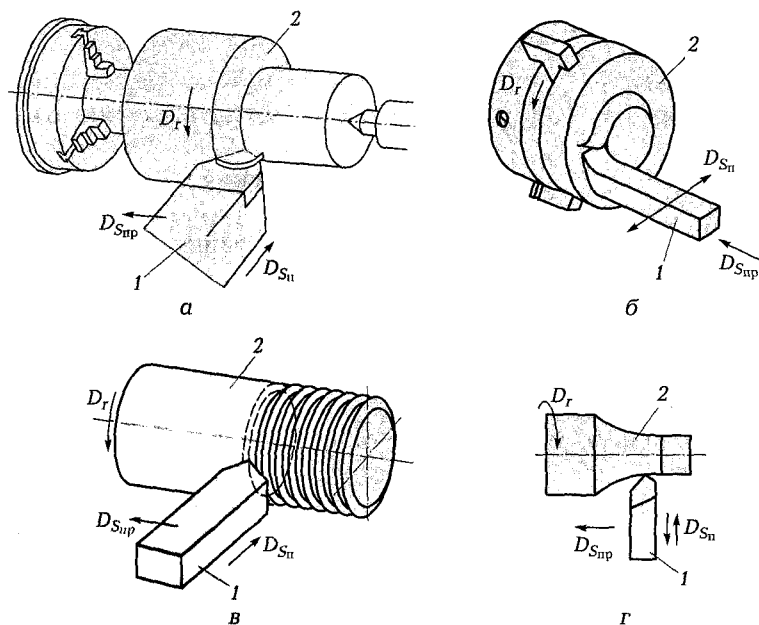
Схемы формообразования поверхностей резанием на токарных станках:
